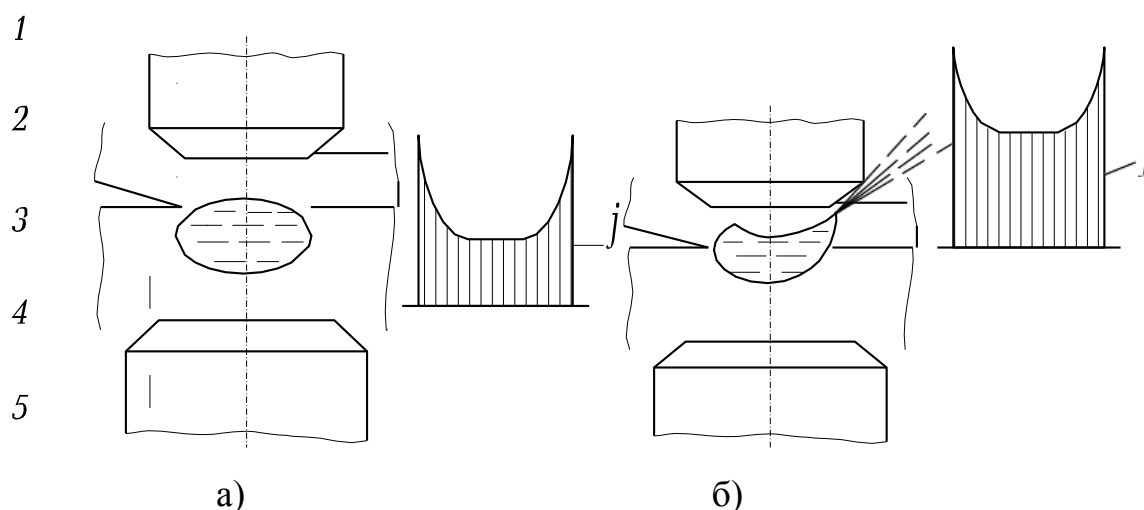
Зона расплавления и плотность тока  $j$  при сварке деталей неравной толщины:
